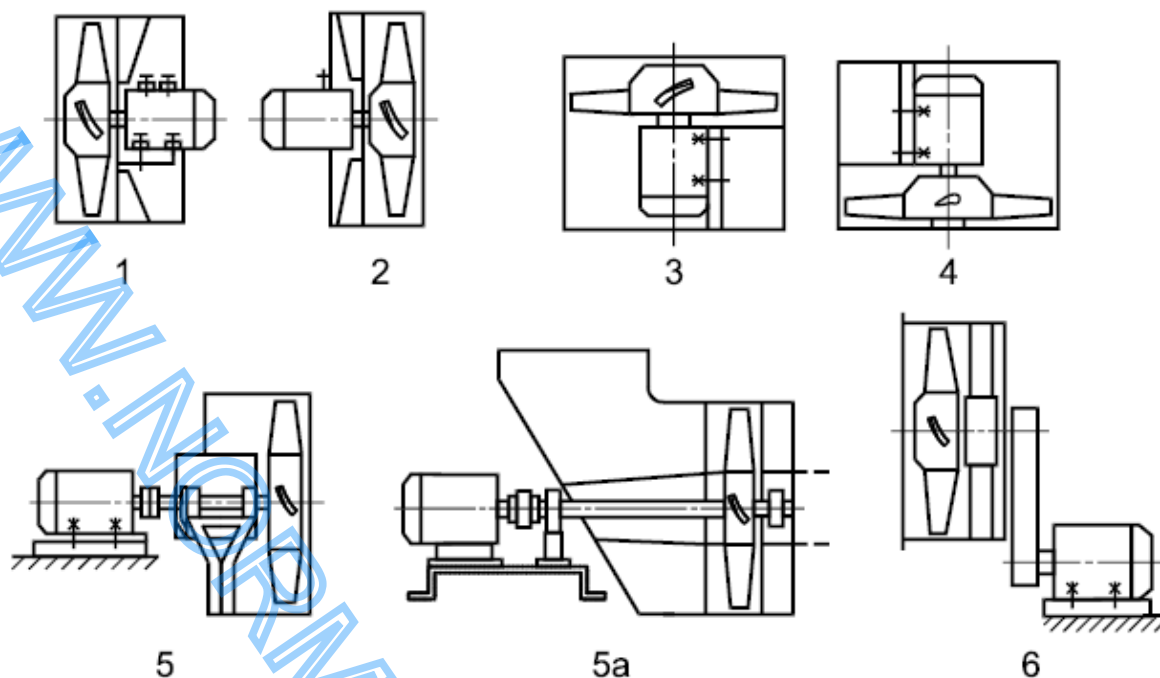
Различные конструктивные исполнения вентиляторов осевых
